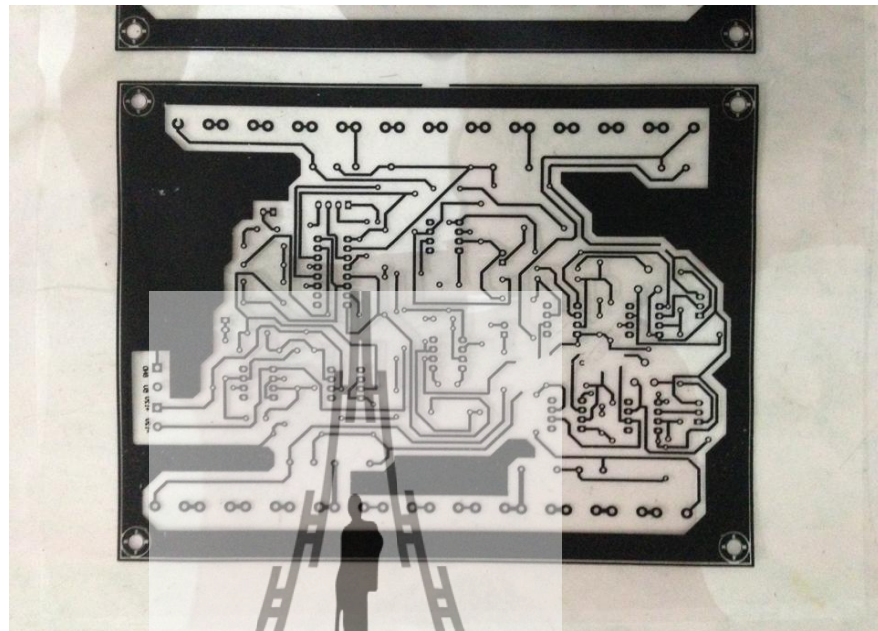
Artwork ของ PCB เพื่อนำไปทำเป็นแผ่น PCB
